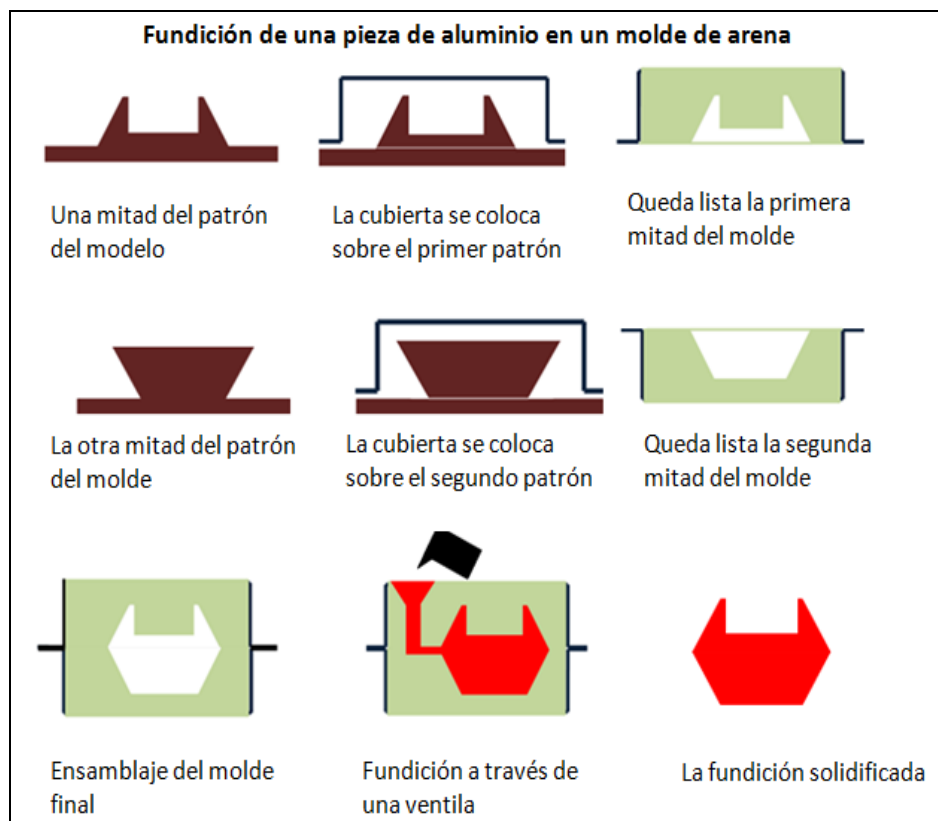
Fundición de una pieza de aluminio en un molde de arena [2].
